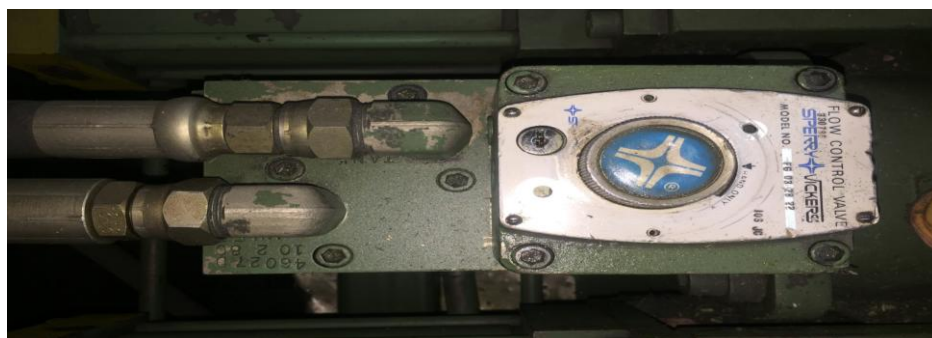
Actuador involucrado en mecanismo de giro de tornillo (motor hidráulico)
